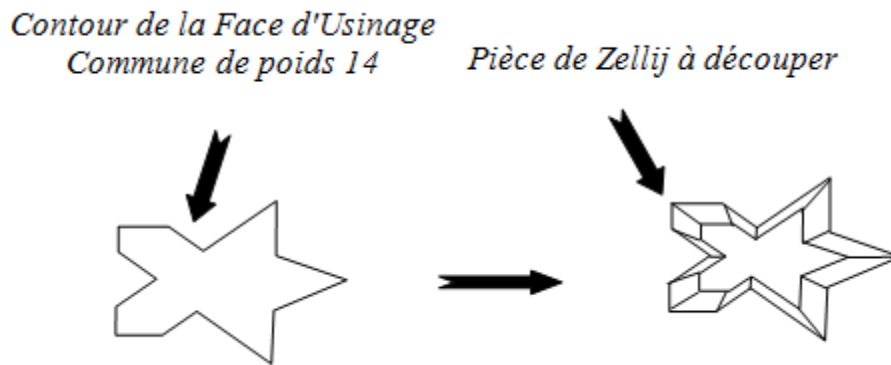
Exemple de Faces d'Usinage Communes d'une pièce de Zellij obtenues à partir d'un modèle de faces frontières.
